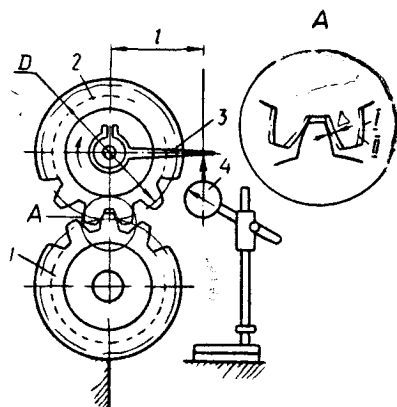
Перевірка бічного зазора в зачепленні циліндричних зубчастих коліс
